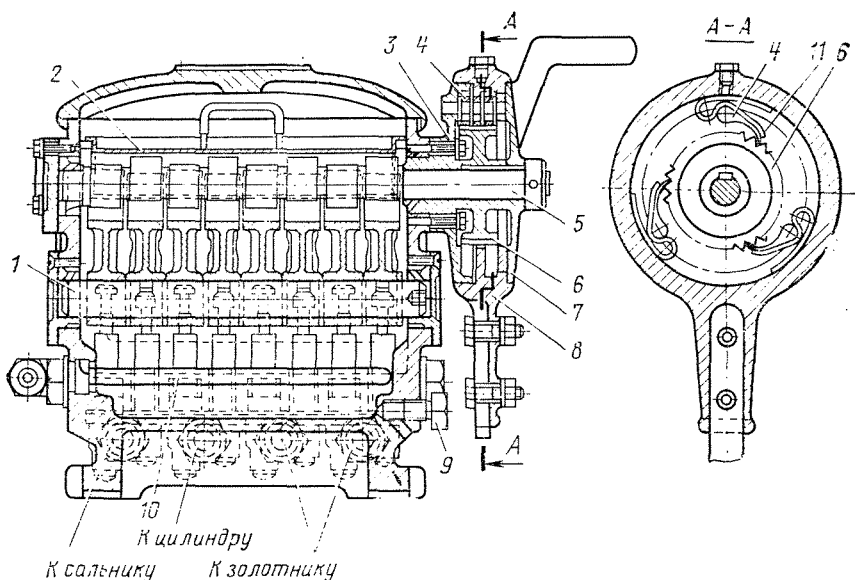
Продольный разрез двухпоршневого масляного пресс-аппарата
